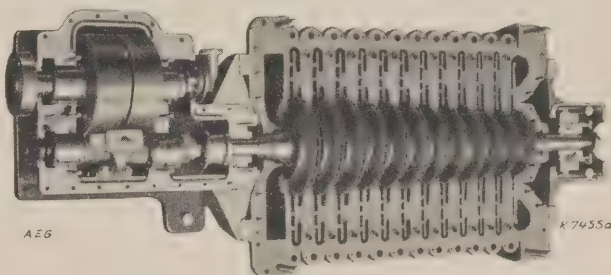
Aufsicht auf die wagerechte Teilfuge der unteren Gehäusenhälfte des Kreiselkompressors Type EK 12 g.
